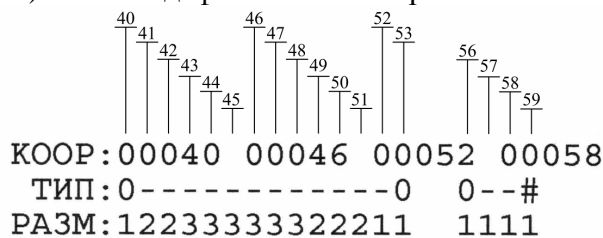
Пример расшифровки протокола автоматизированного контроля стыковых и тавровых сварных стыковых соединений толщиной до 10мм.
